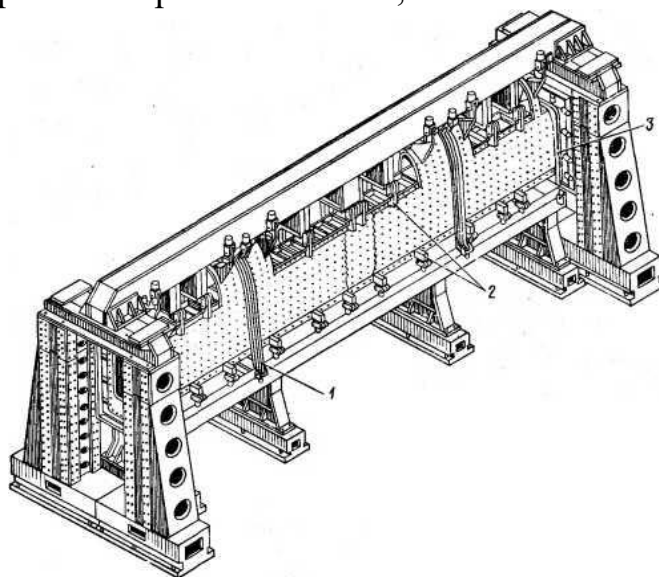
Приспособление для сборки кессона центроплана:
